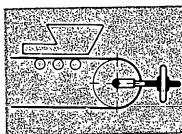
Spanschrauben mit angetriebener Schraubenspindel
